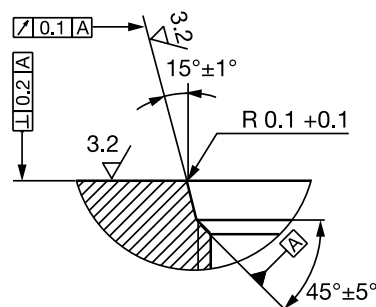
Einschraubloch für die Montage des BTL mit O-Ring
